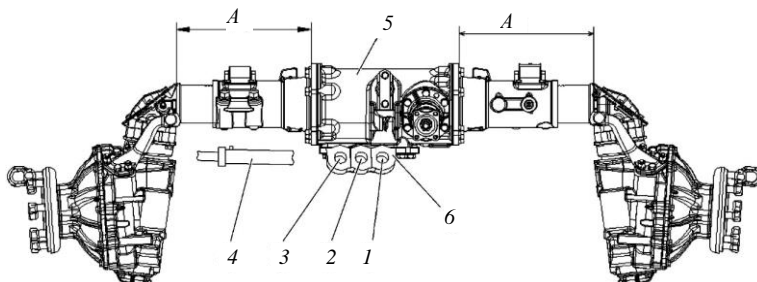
Схема переднего моста трактора с коническими колесными редукторами: 1, 2, 3 – отверстия для крепления цилиндра; 4 – цилиндр; 5 – ПВМ; 6 – кронштейн
